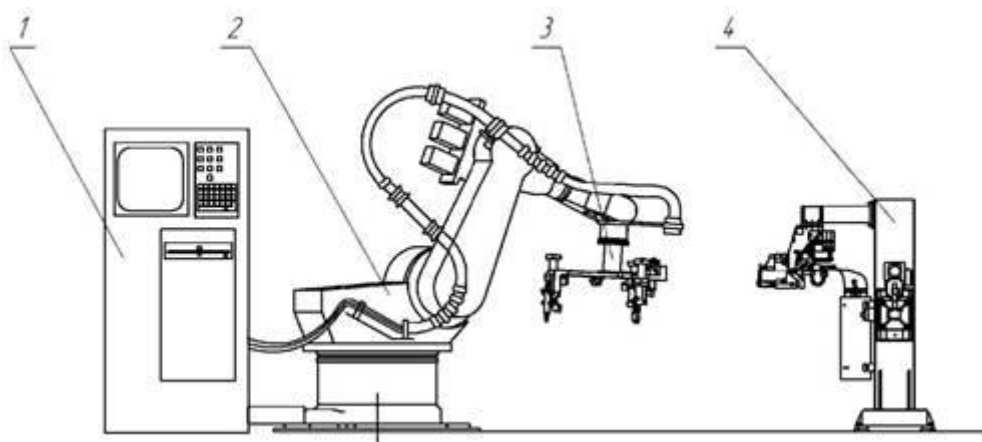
Использование промышленного сварочного робота при контактной точечной сварке
